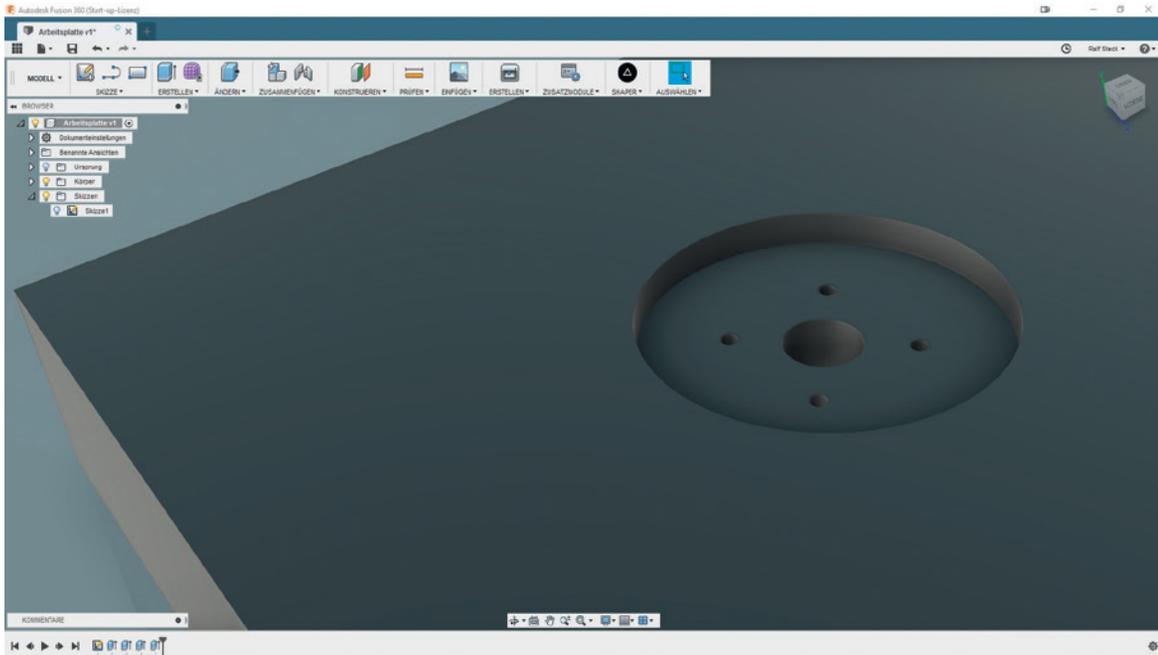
So sollen unsere Fräsungen später aussehen.
